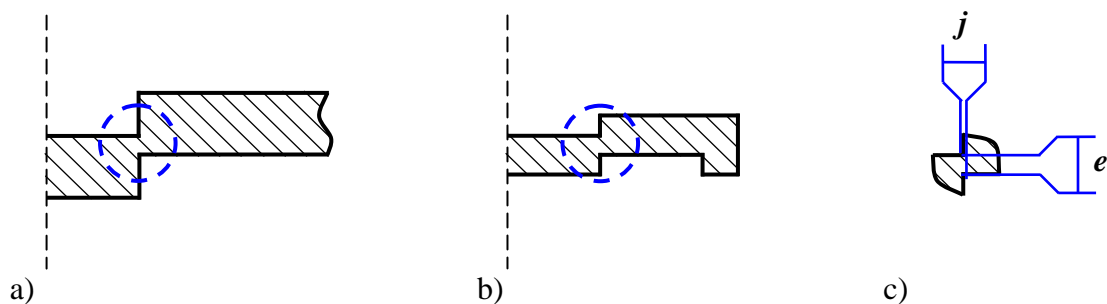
a) Eprouvettes obtenues par semi-découpe. b) Eprouvettes obtenues par usinage. c) Géométrie locale des éprouvettes.
